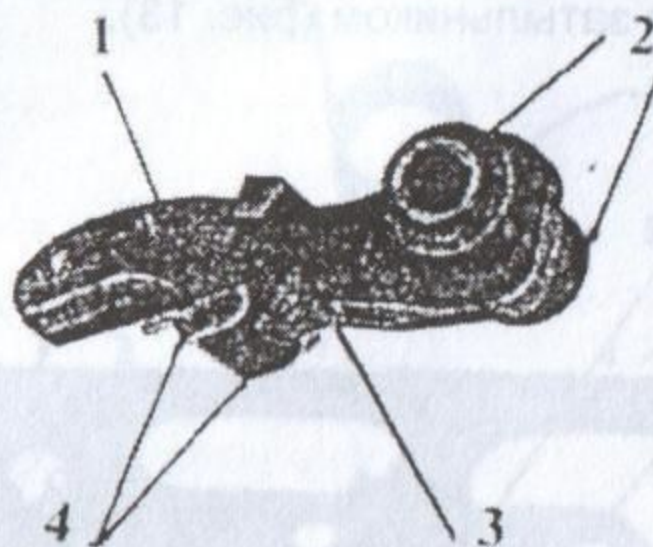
Курок: 1 — рабочая поверхность; 2 — цапфы; 3 — выступ для автоспуска; 4 — выступы для зацепов спускового крючка и шептала
